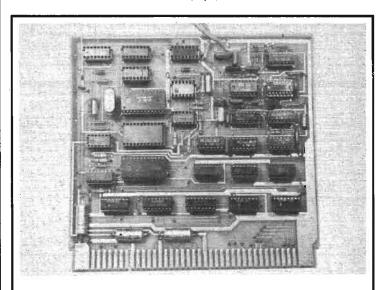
Photo E. - Carte ISA non équipée en RS232, CI FACIM.
